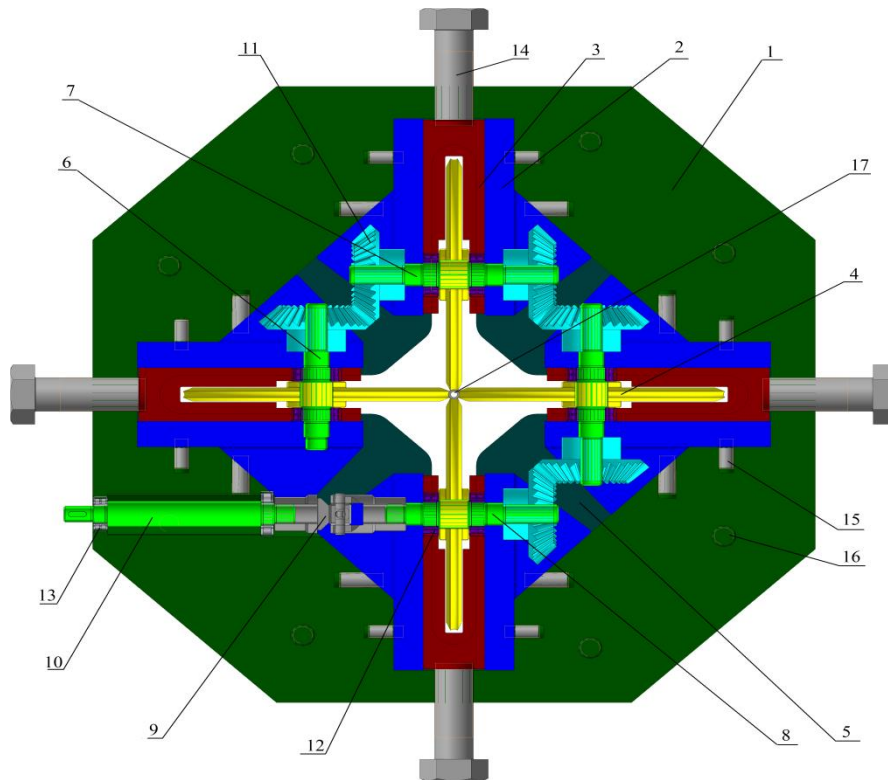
Конструктивна схема 4-валкової кліті для профілювання внутрішньої поверхні трубчастої заготовки:
